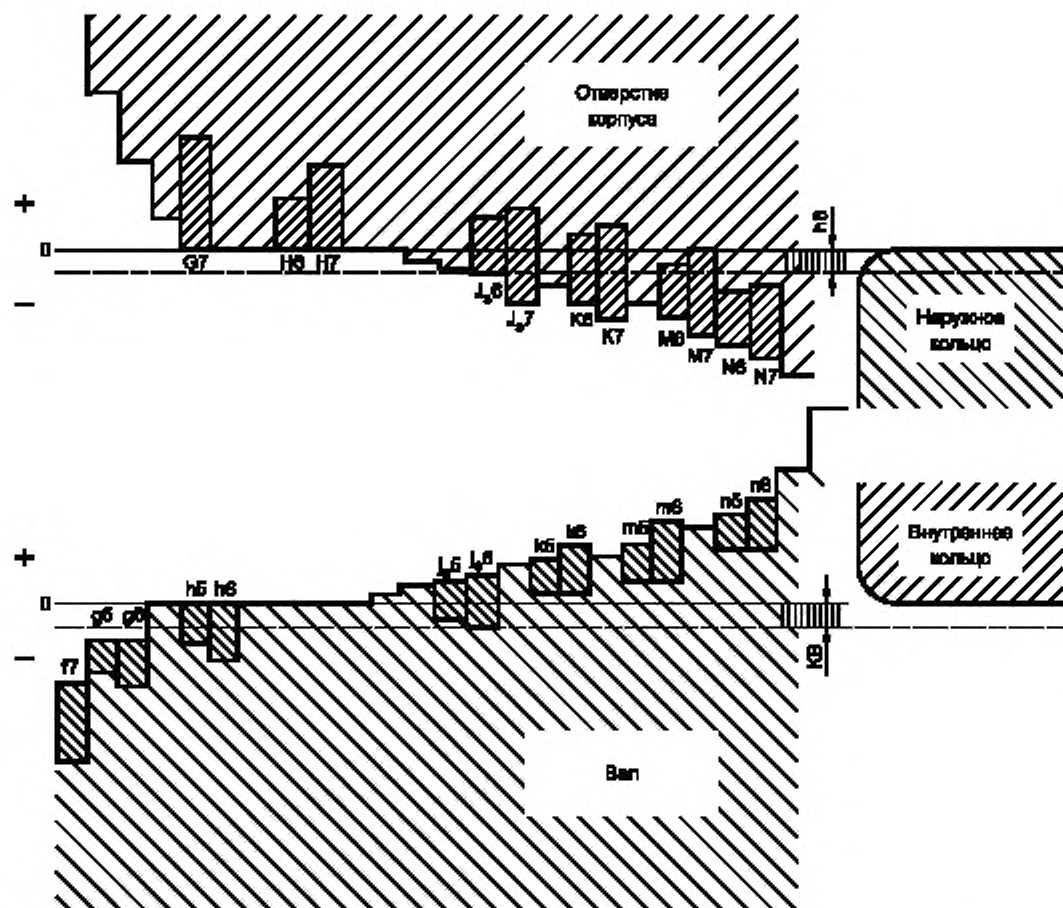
Поля допусков колец подшипников, валов и отверстий корпусов при различных посадках
